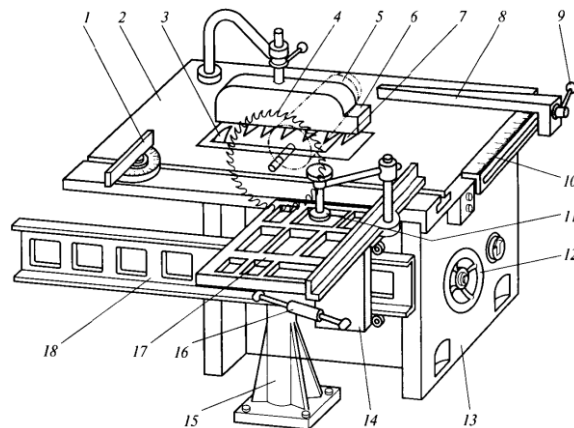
Універсальний круглопилковий верстат для змішаного розкрою: 1 – косинець; 2 – стіл; 3 – розклинювальний ніж; 4 – пилка; 5 – електродвигун; 6 – огороження; 7 – кігтевий захист; 8 – напрямна лінійка; 9 – рукоятка фіксатора; 10 – лінійка; 11 – притиск; 12 – маховичок підйому пилки; 13 – станина; 14 – каретка; 15 – стійка; 16 – стяжка; 17 – стіл каретки; 18 – напрямна
